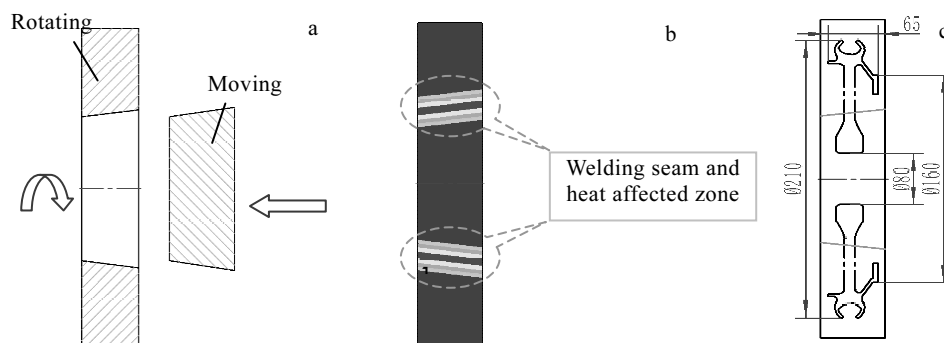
IMI834/Ti6246 双合金惯性摩擦焊接示意图
